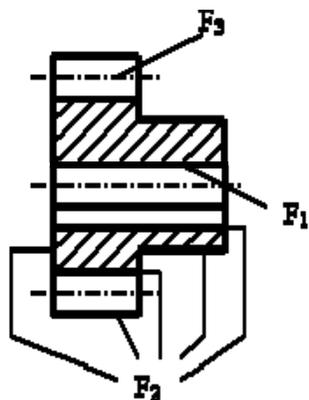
Эскиз детали «Зубчатое колесо»
